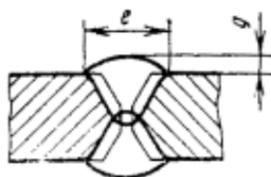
Эскиз сварного шва с обозначением превышения и ширины шва
